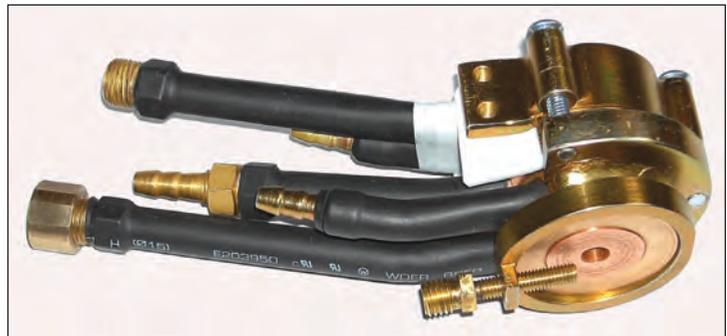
Плазмотрон для напыления покрытий на внутренние поверхности гильз судовых и локомотивных двигателей
